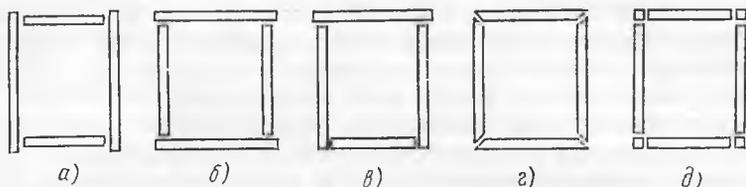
Схемы типовых расположений стенок корпусной мебели:
